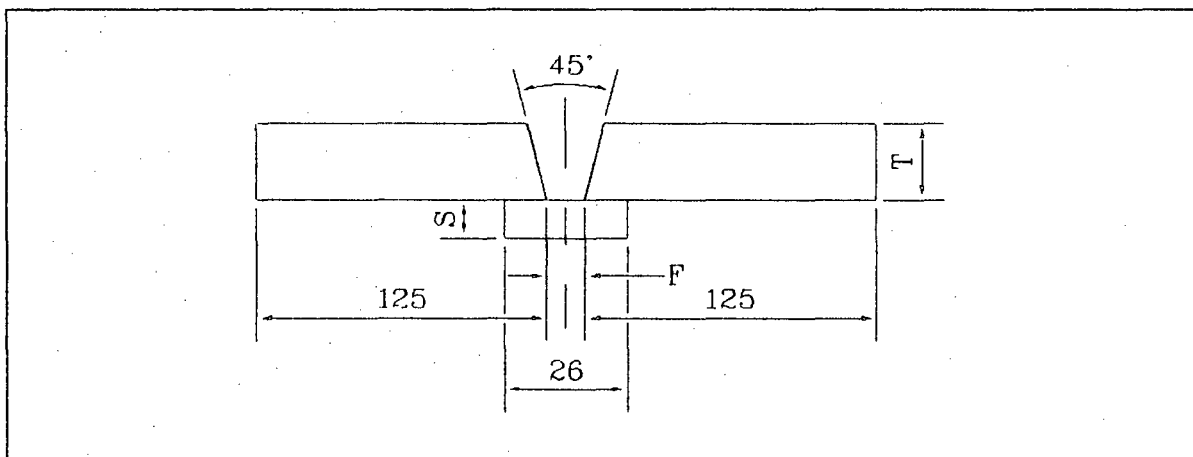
Corte da seção transversal do corpo de prova "ENSAIO". Dimensões em mm.
